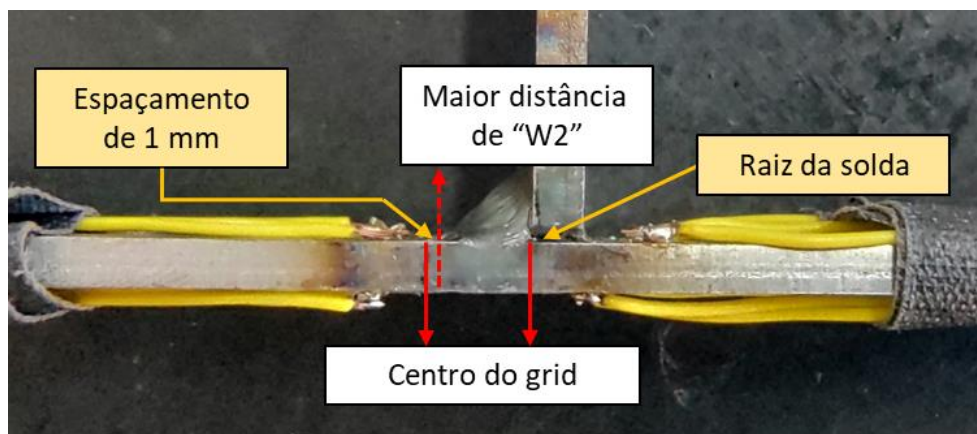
Posicionamento dos SGs no CDP metal soldado sem ponto de solda
